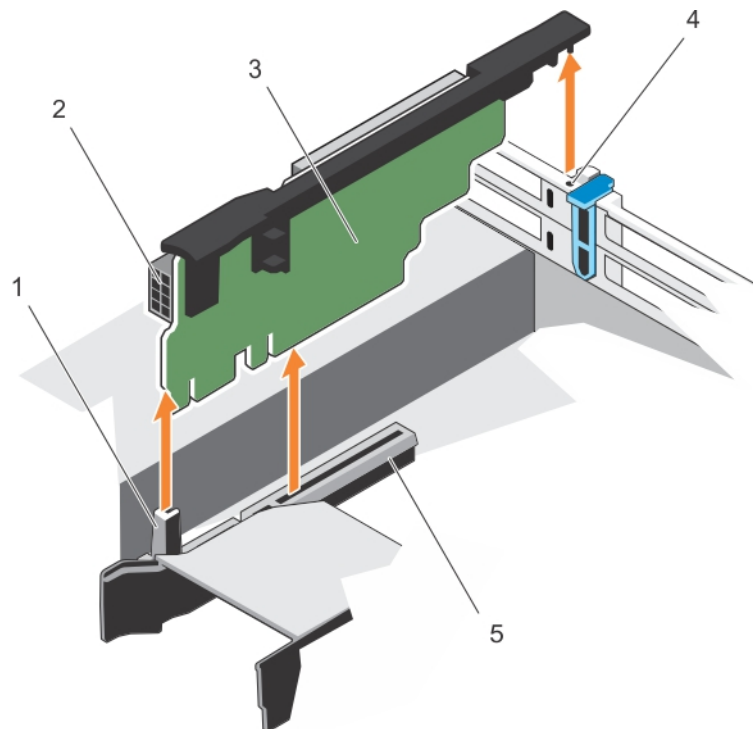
Como remover e instalar a riser da placa de expansão 2
